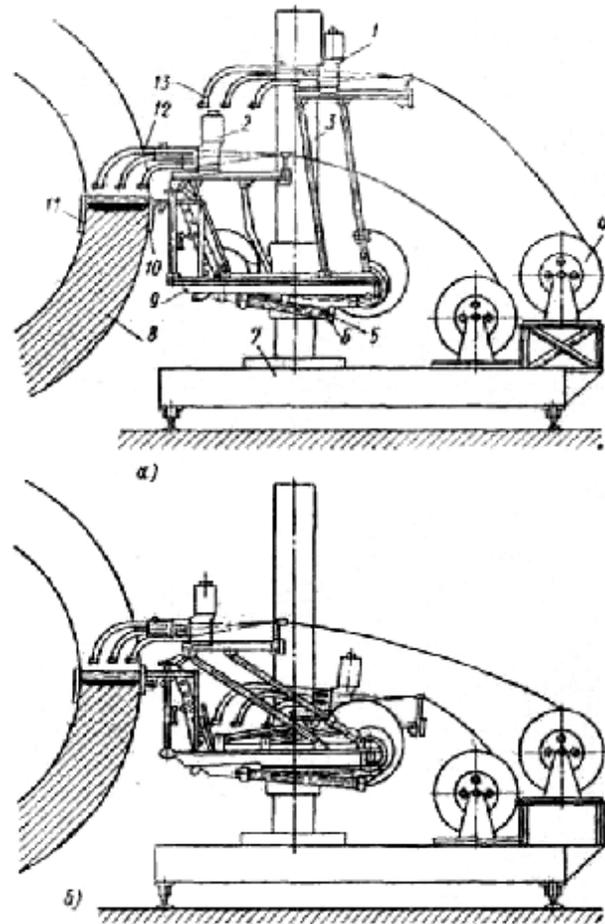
Схема сдвоенного аппарата: *а* — положение сварочных головок до дублирования; *б* — положение сварочных головок после дублирования; 1 — сварочная головка до дублирования (положение 1); 2 — сварочная головка 2 до дублирования (положение 2); 3 — колонна; 4 — кассета с проволокой; 5 — уравнивающая пружина головки 2; 6 — уравнивающая пружина головки 1; 7 — тележка; 8 — свариваемая заготовка; 9 — площадка для сварщика-оператора; 10 — наружное охлаждающее устройство (охладитель); 11 — внутреннее охлаждающее устройство; 12 — мундштук к головке 2; 13 — мундштук к головке 1
